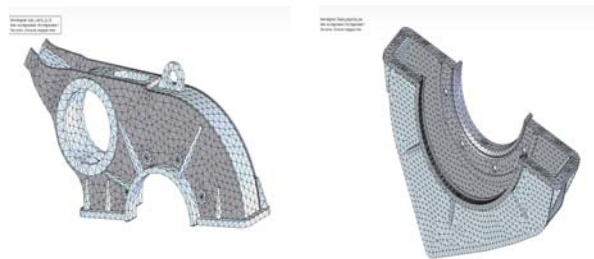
Розрахункові скінченно-елементні схеми корпусу редуктора
